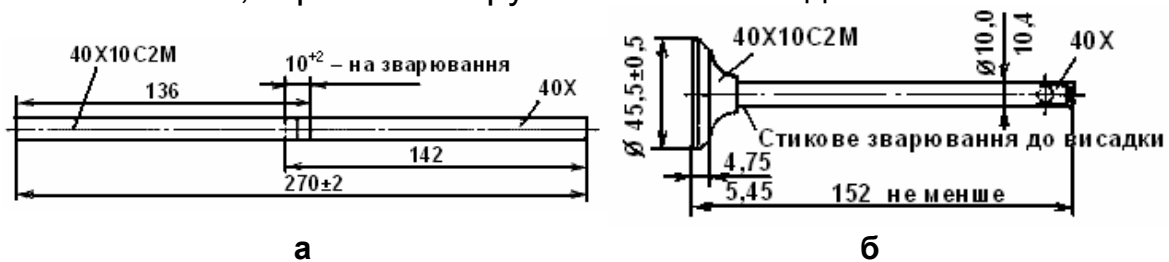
Заготовка клапана (а) і готова деталь (б) із різних матеріалів
